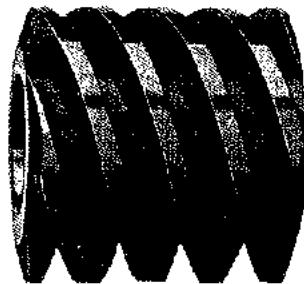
Tornillo sin fin (Boston Gear Works)
